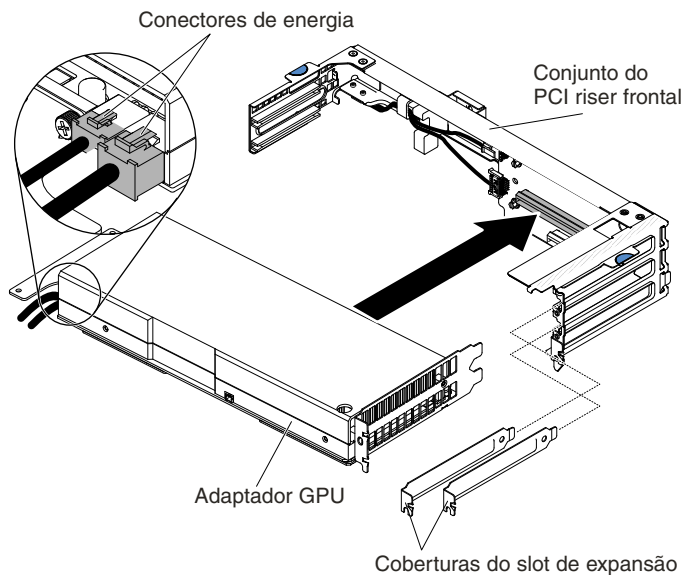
Instalação do adaptador GPU (no conjunto da placa riser PCI frontal)
